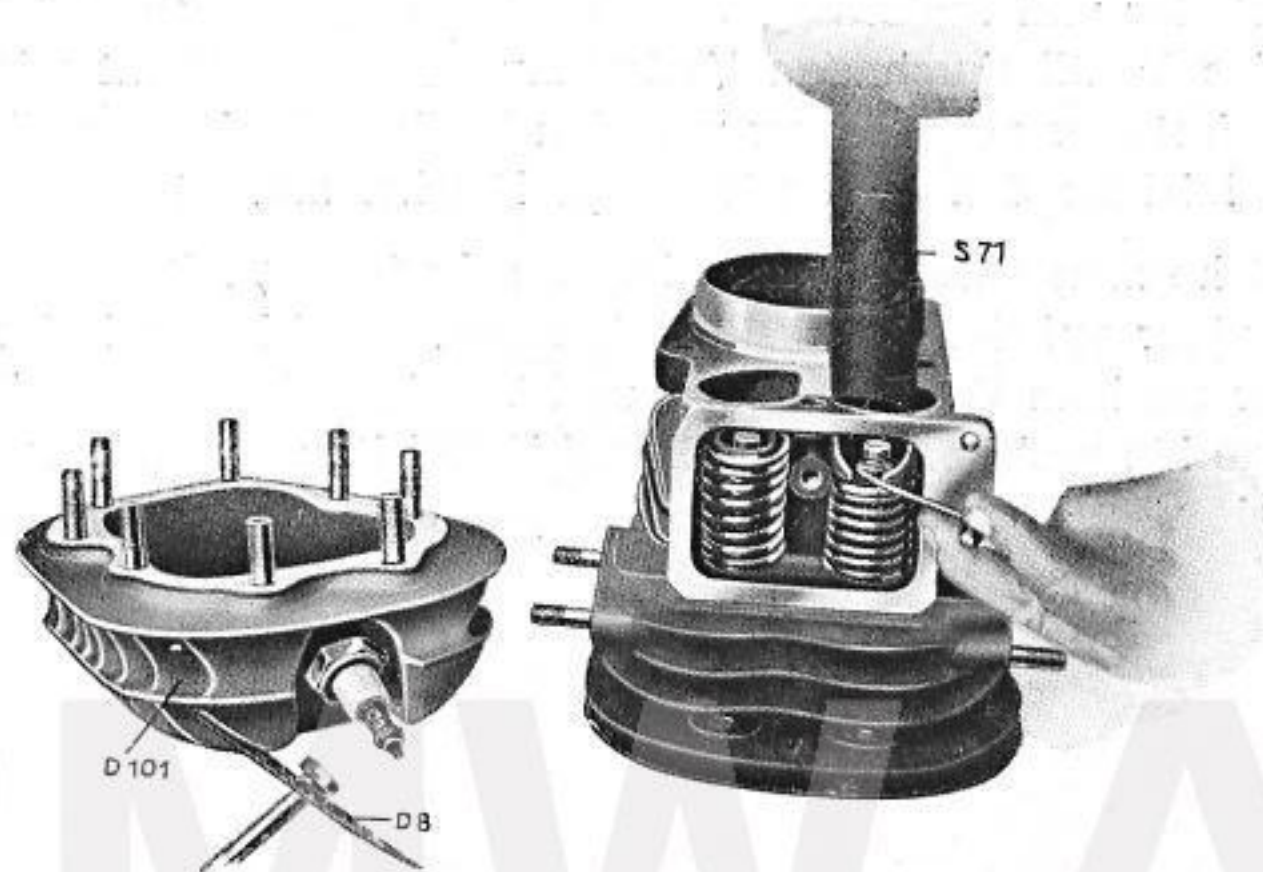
Ausbau der Ventile bei der Tourenmaschine
